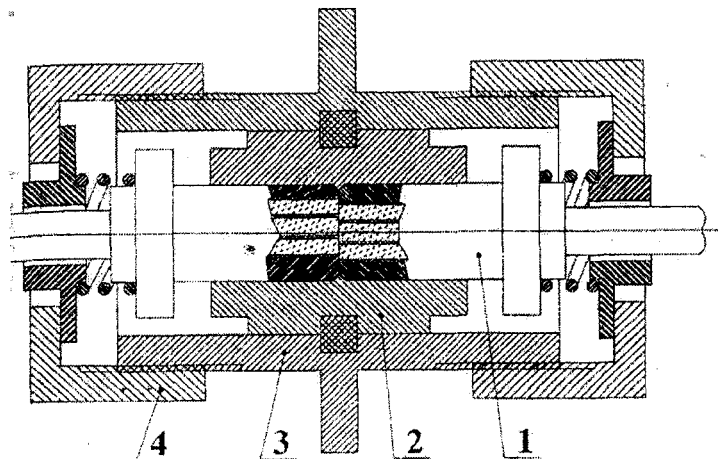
Схема конструкції роз'ємного багатомодового ОЗП
